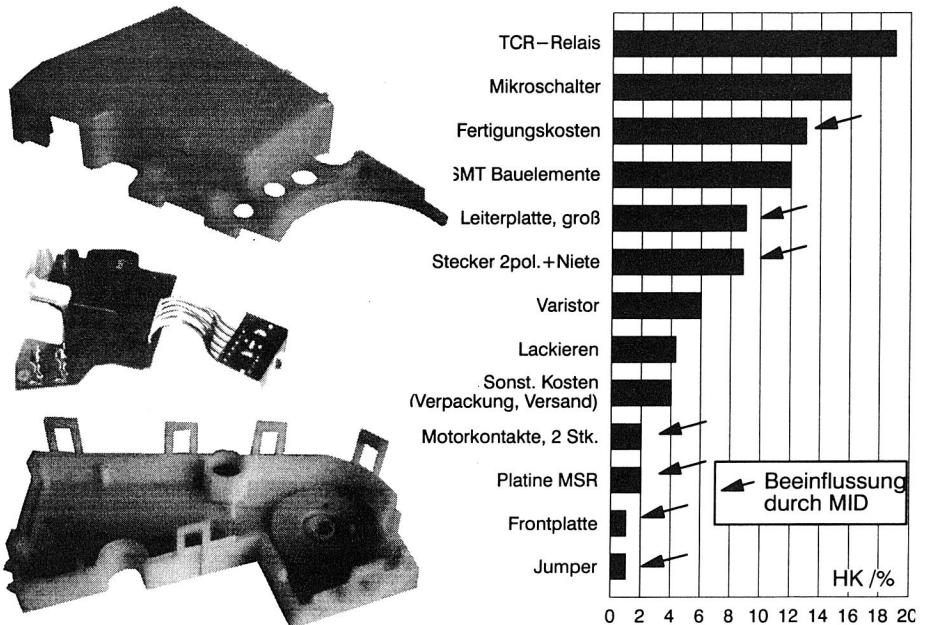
Konventionelle Aufbautechnik des E-Moduls
